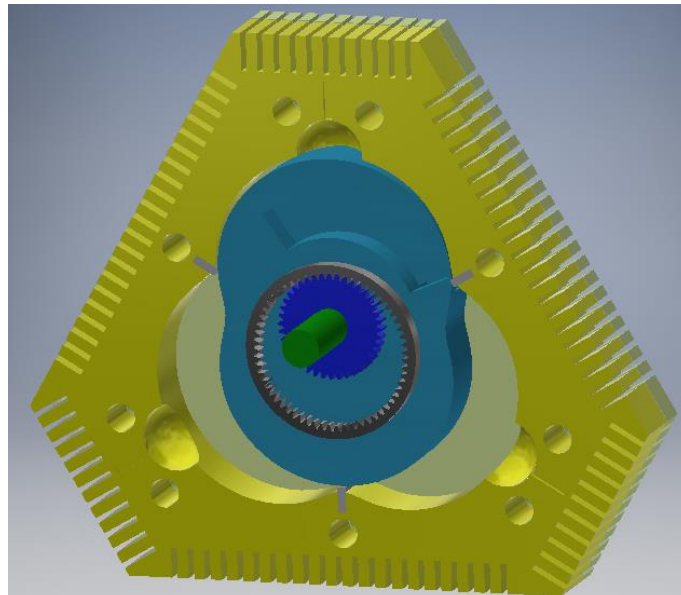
Inici de l'ensamblatge amb estator i rotor.
